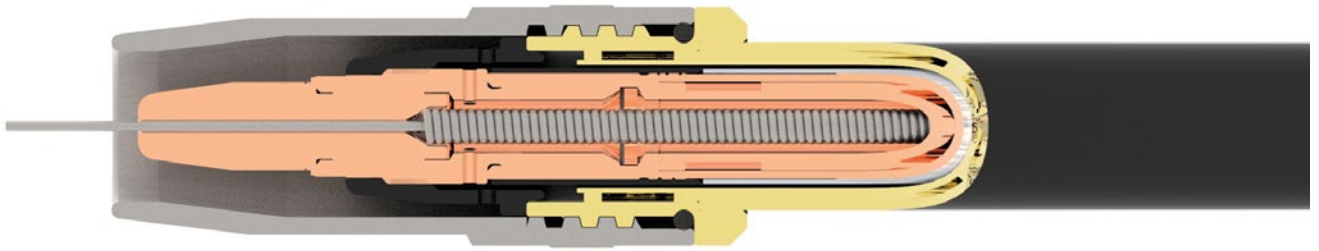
Schnittbild eines MIG/MAG-Schweißbrennerkopfes
